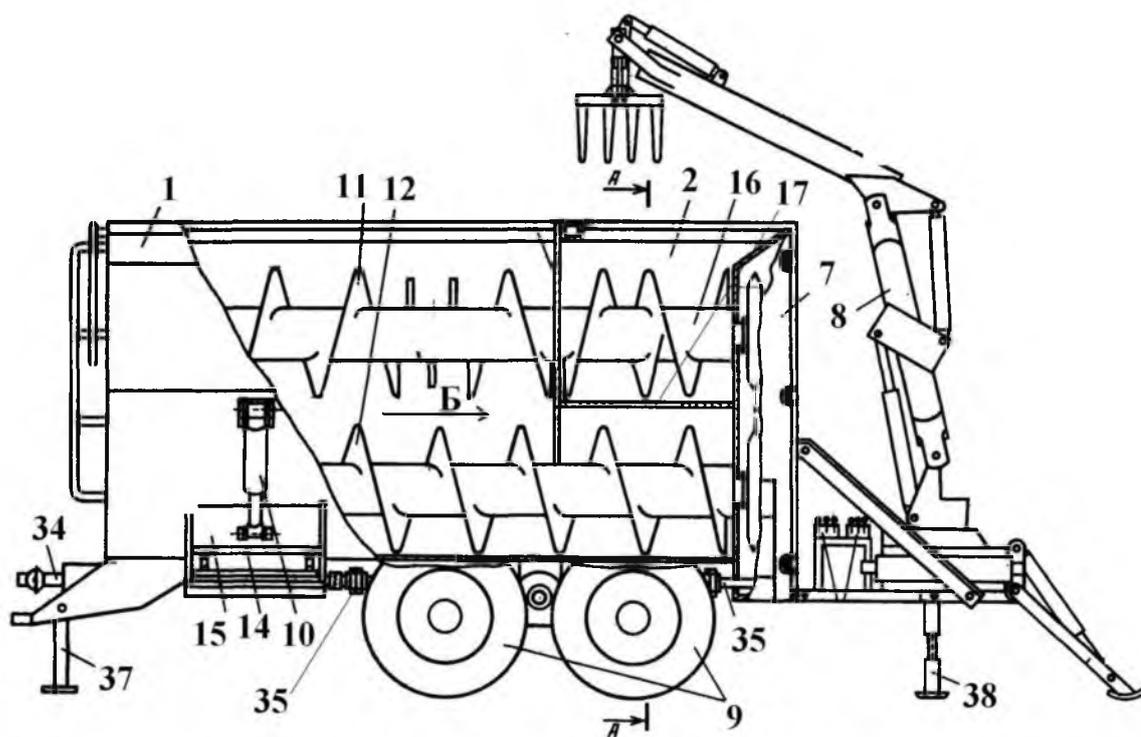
Мобильный кормоприготовительный агрегат (вид сбоку):
